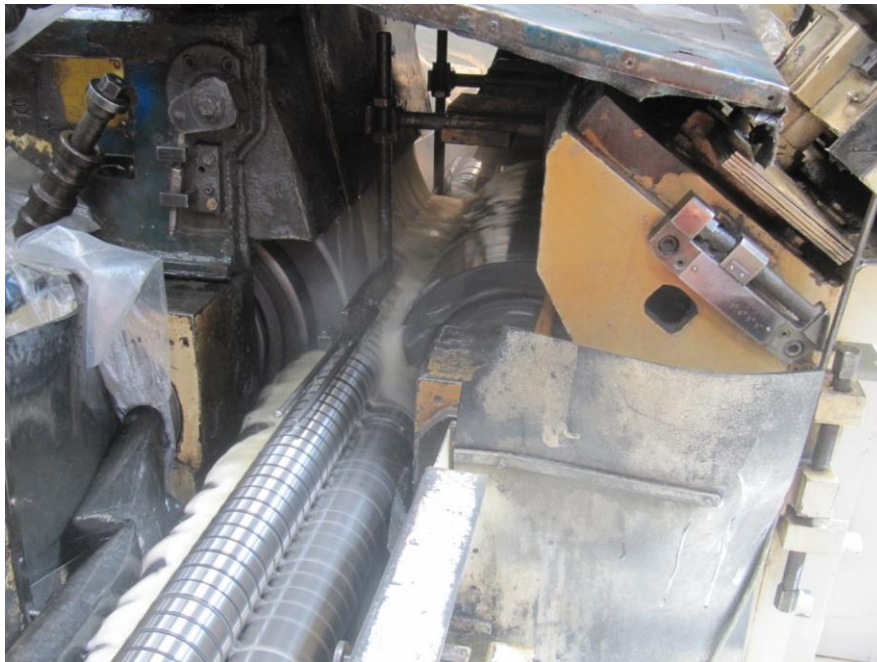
Загальний вигляд робочого простору безцентрово-шліфувального верстата
